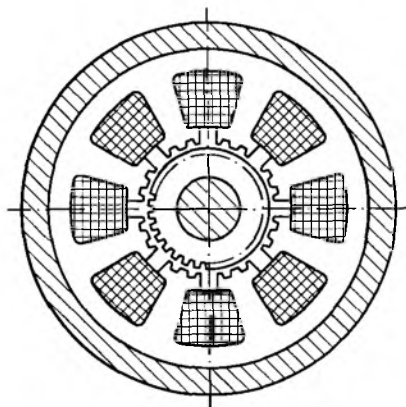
Устройство реактивного шагового двигателя с редукцией скорости
